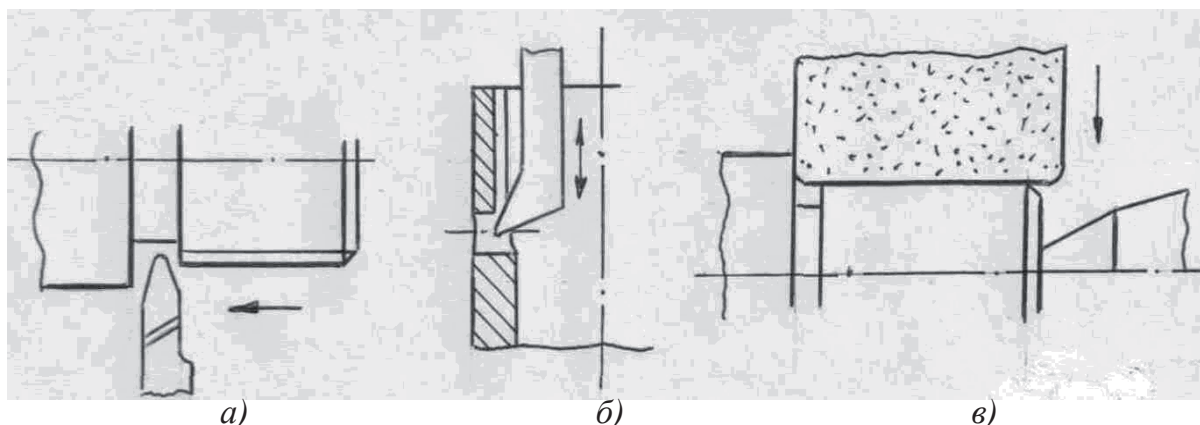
Наличие канавок для выхода режущего инструмента, определяющих технологичность деталей: *а* – для выхода резьбового резца; *б* – для выхода долбежного резца; *в* – для выхода шлифовального круга
